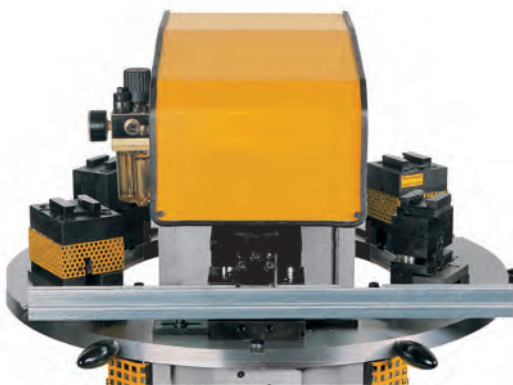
R Mehrfachstanze mit Revolver für 6 Werkzeuge
